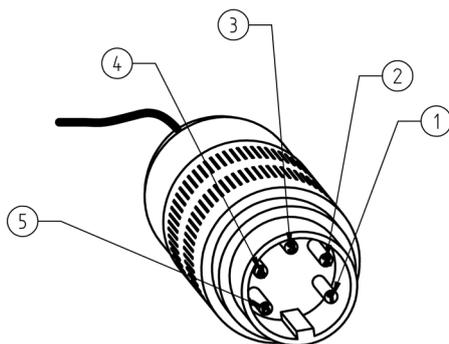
Sonde Combinée KS1D ECO (dimensions en mm)
